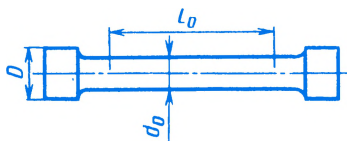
Цилиндрический образец типа I, II, III для испытания на статическое растяжение с основными размерами, мм:
